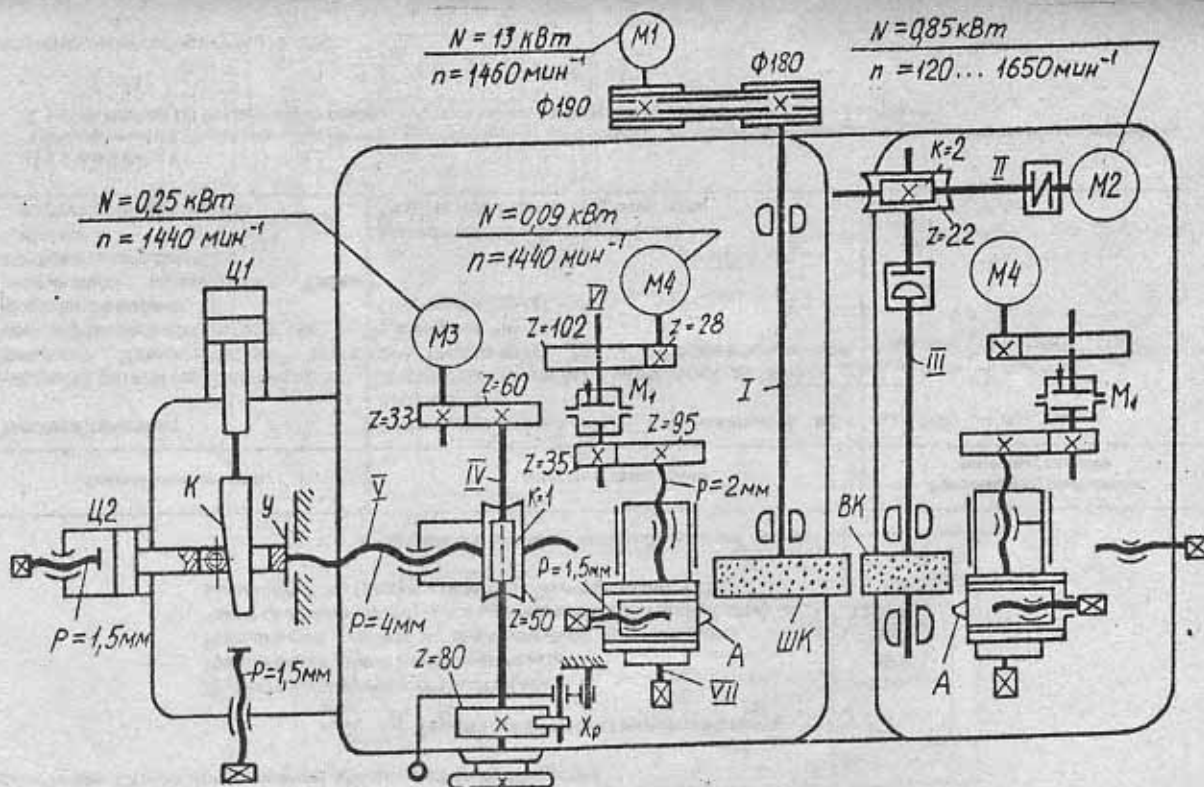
Кинематическая схема бесцентровошлифовального станка мод. 3М184
